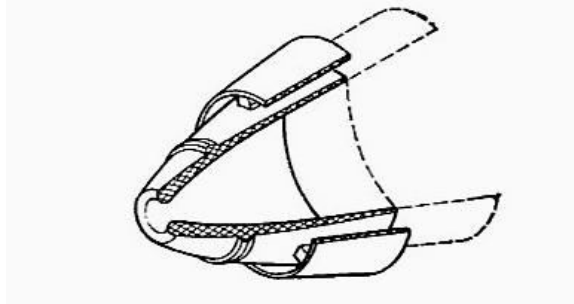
Сопла с жесткими выдвигаемыми насадками
